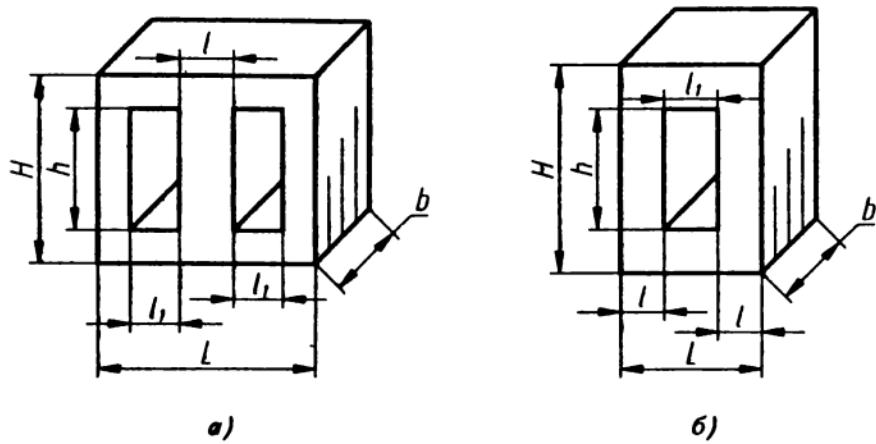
Размеры магнитопроводов пластинчатой конструкции:
